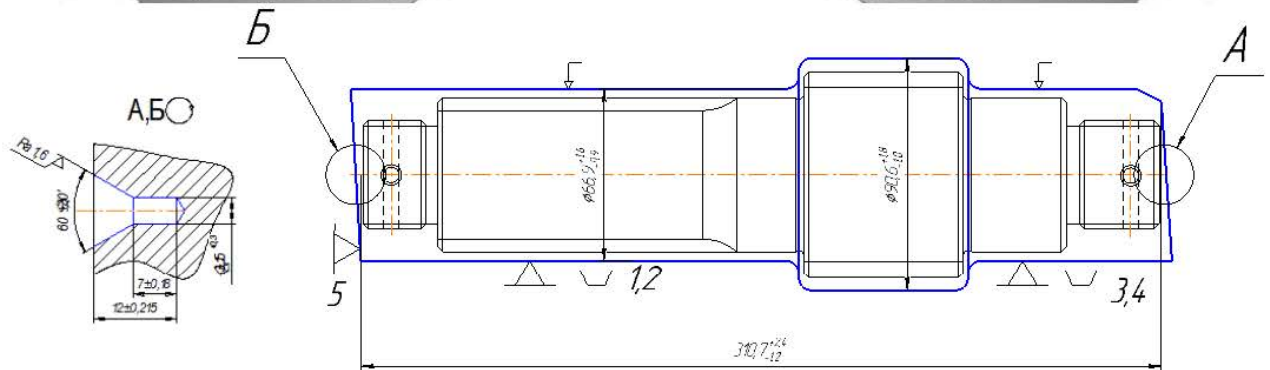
Базування вала ведучого на фрезерно-центрувальній операції 010
